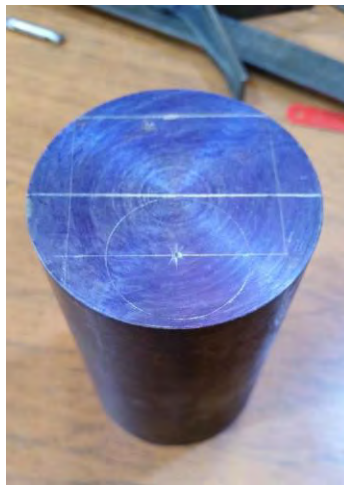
Trazado sobre la superficie de la pieza a trabajar para fabricar opresor de tubo 29mm.
